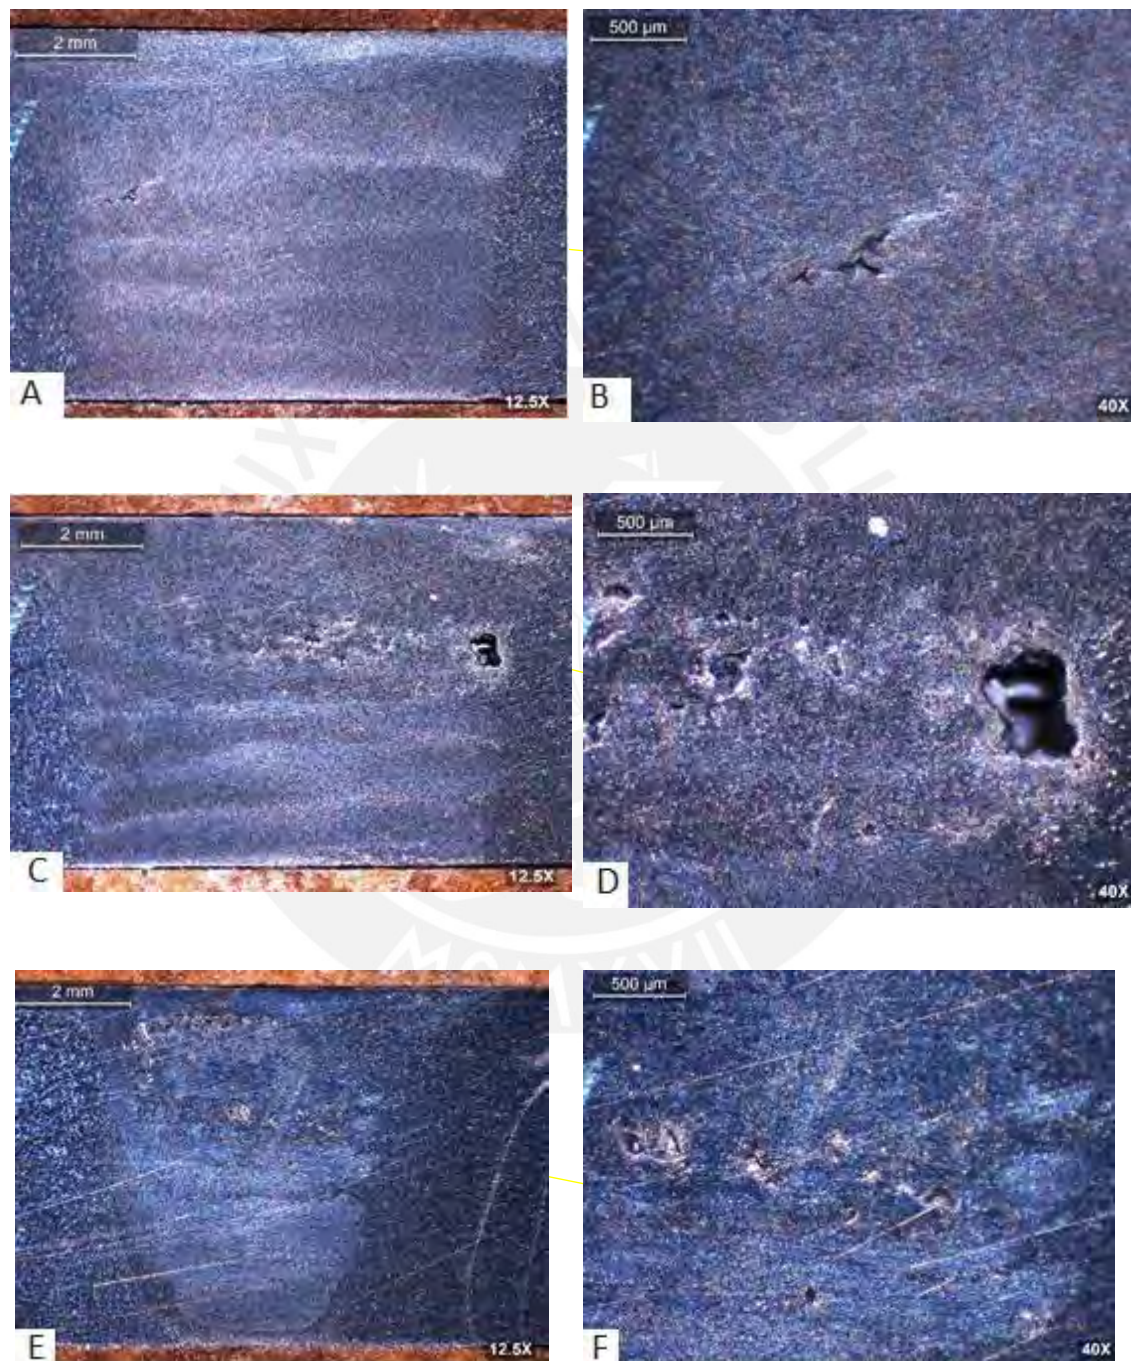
Macrografía muestras de defectos en zona soldada ejecutadas con pin Mx Trivex A-B : probeta soldada 1850/40, C-D: probeta soldada 1900/40, E-F: probeta soldada 1950/40.
